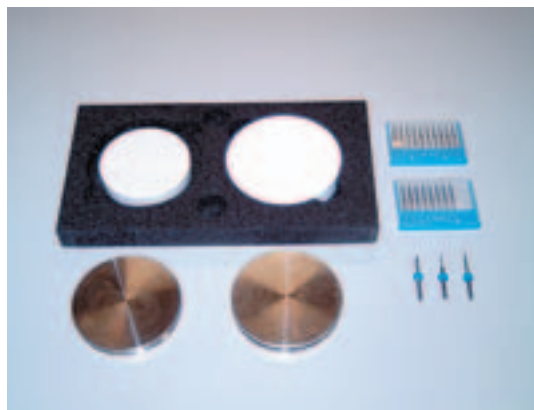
Materialauswahl für die i-mes-Fräsmaschine.
